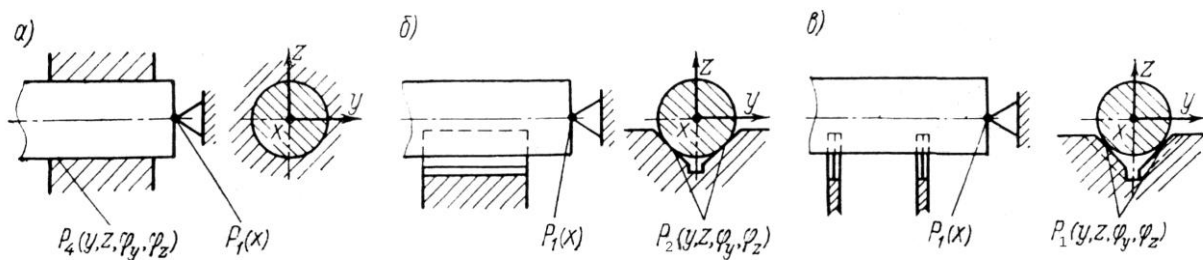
Вихідні схеми базування тіл циліндричної форми із зв'язками:
